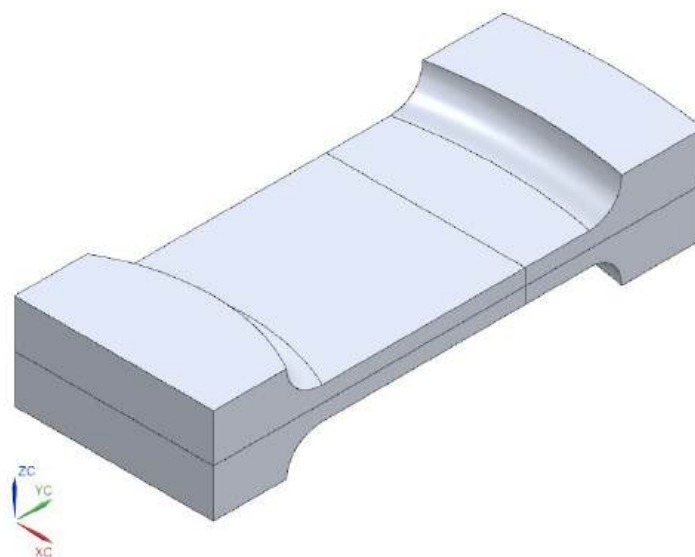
Образец-имитатор спинки рабочей лопатки
